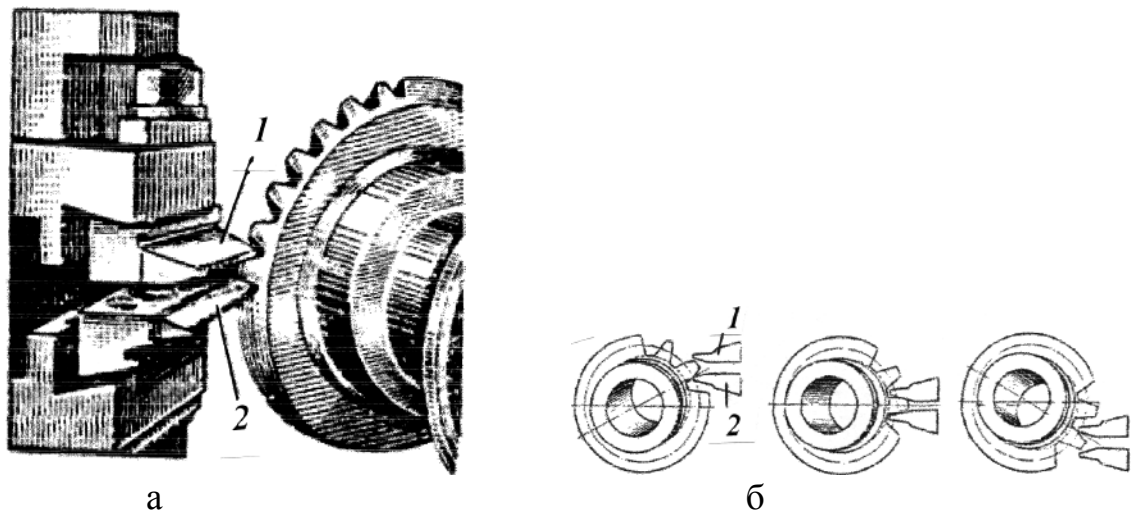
Нарезание конического зубчатого колеса на зубострогальном станке: а - установка резцов; б - схема обкатки; 1 и 2 – резцы.
